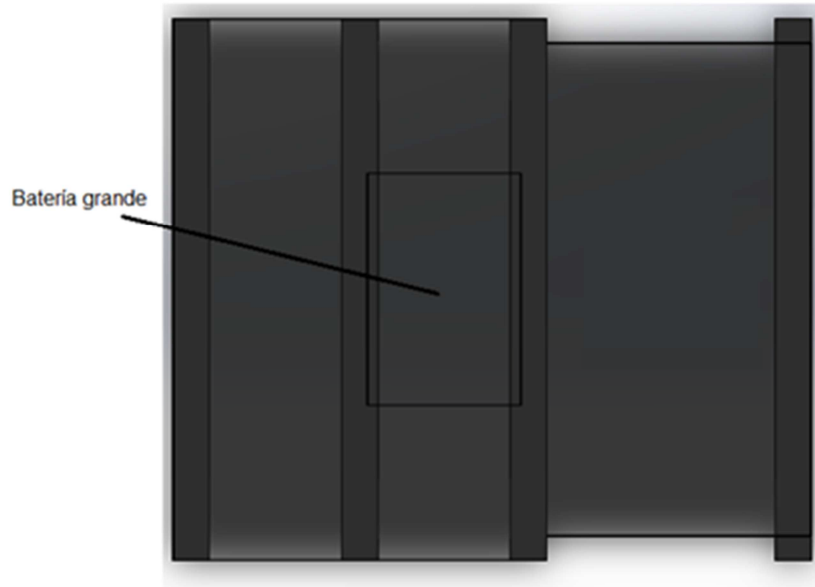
Ubicación de las baterías en su plancha de soporte.
